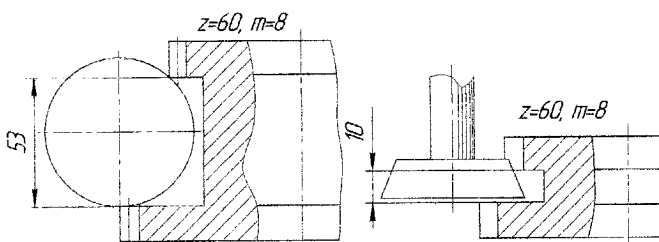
Мінімальний вихід інструменту для нарізування блокових зубчастих коліс: а) черв'ячною фрезею; б) довбачем
